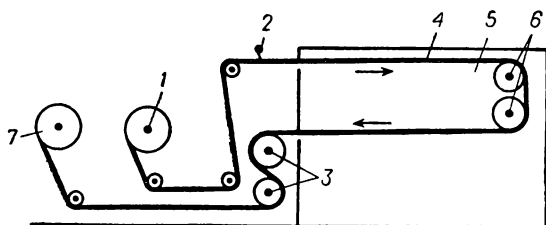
Схема движения ткани при изготовлении ковров на губчатой основе в машине конструкции НИИРа:
